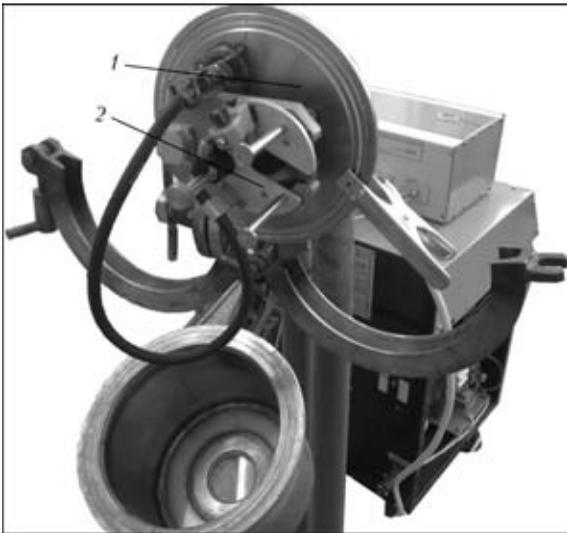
Внешний вид камеры (1) и сварочной головки АДЦ 627.03.00.000 (2)
